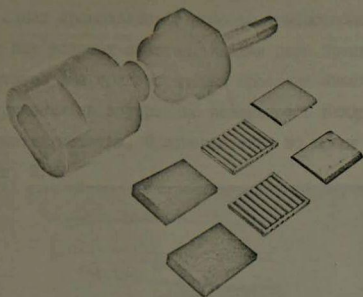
Промежуточные захваты с роликовыми обоймами.
